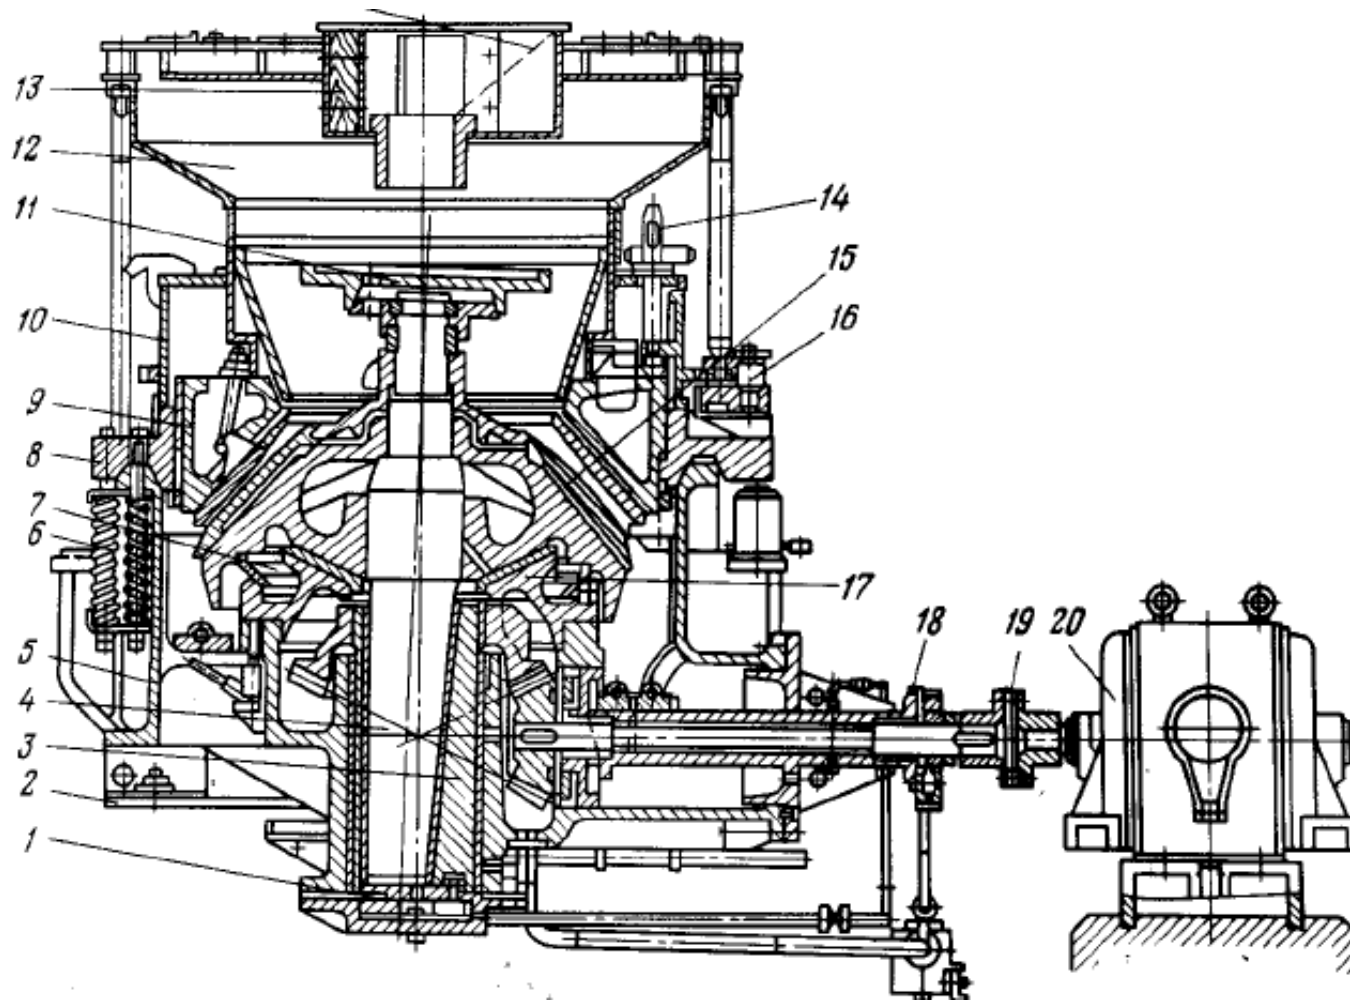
Принципова схема конусної дробарки середнього та дрібного дроблення:
